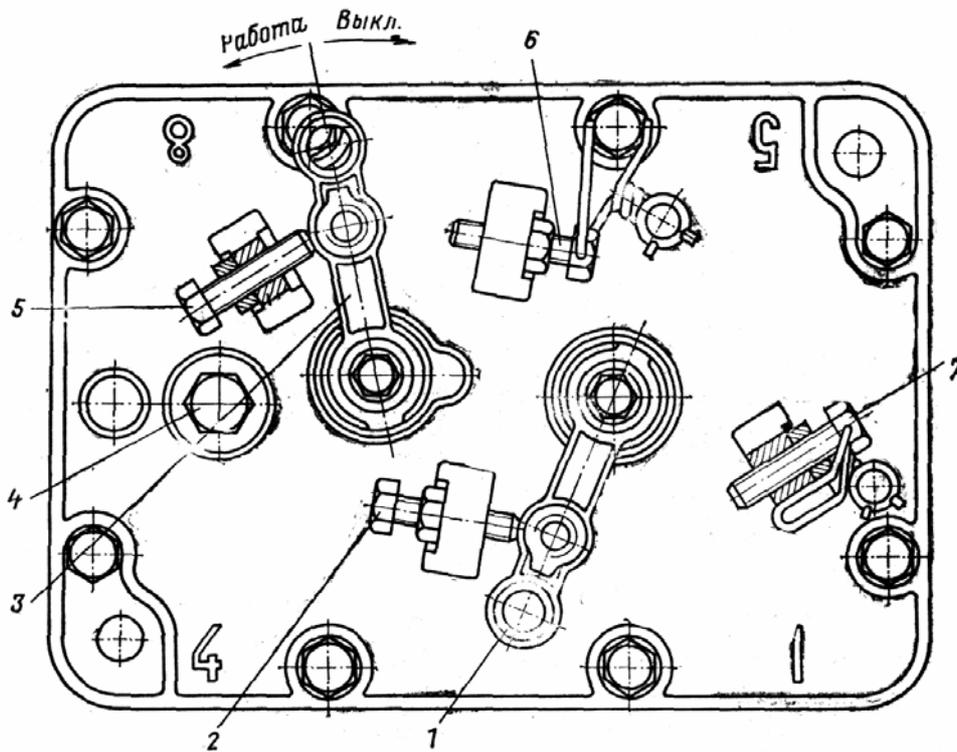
Крышка регулятора с рычагами подачи топлива и останова двигателя:
